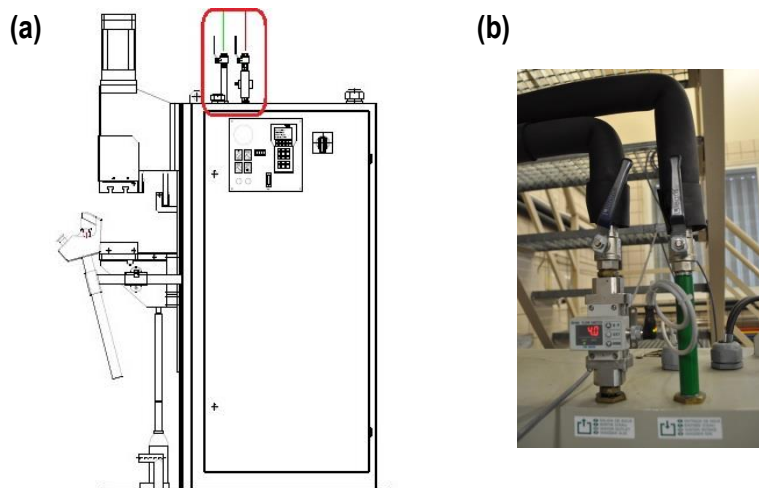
a) Ubicación y b) detalle del caudalímetro de la máquina de soldadura.
